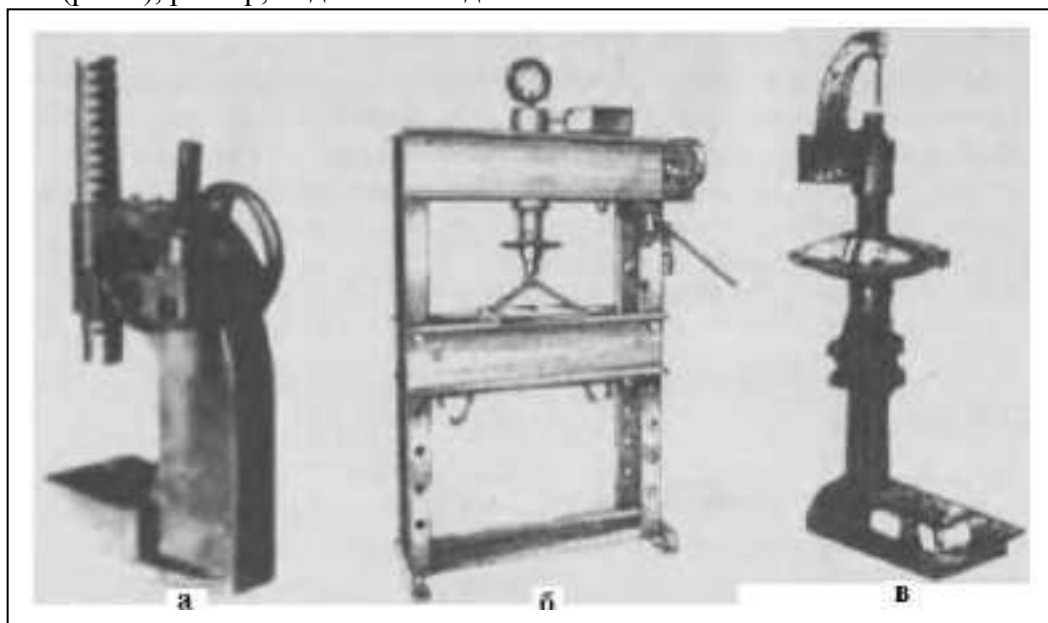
Различные прессы для разборочно-сборочных работ: *а* — электрогидравлический напольный пресс 2135-1М с дополнительным плунжерным насосом и ручным приводом для разборки и сборки мелких узлов; *б* — пневматический напольный пресс Р-304 для клепки
